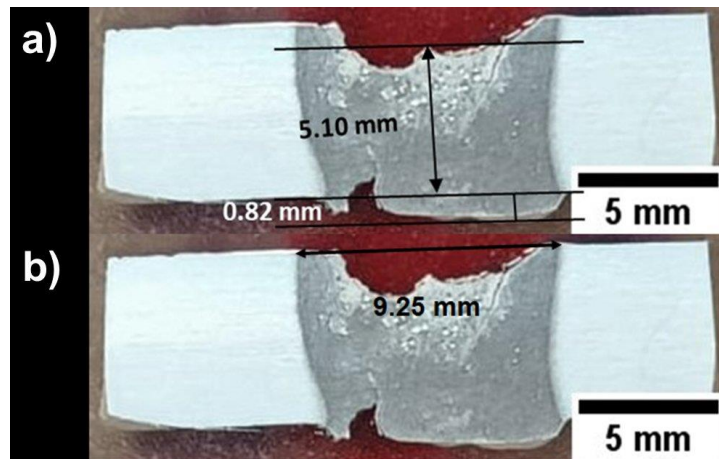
89 Geometría de la réplica del cordón de soldadura número 12, cuyos valores son a) 5.10 mm de penetración y 0.82 mm de concavidad de la raíz y b) 9.25 mm de ancho del cordón de soldadura.
